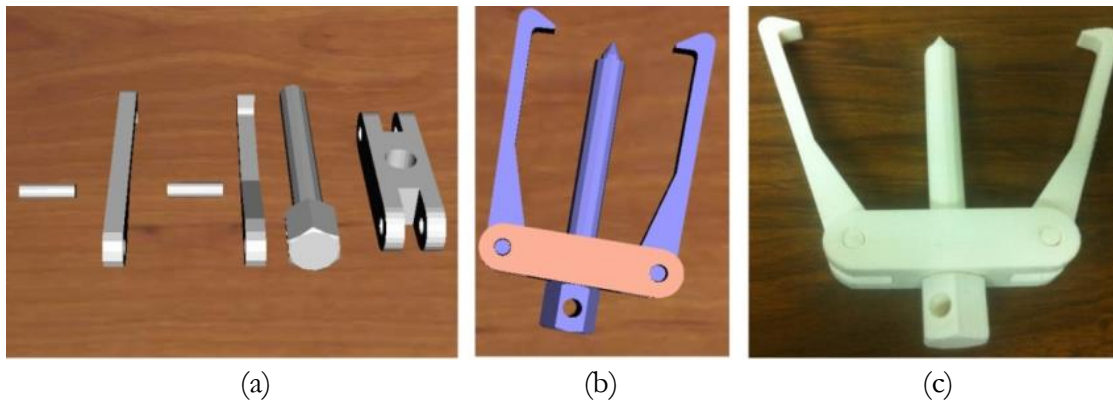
Ensamble del extractor de poleas: (a) piezas sin ensamblar; (b) ensamble virtual; (c) ensamble real.
